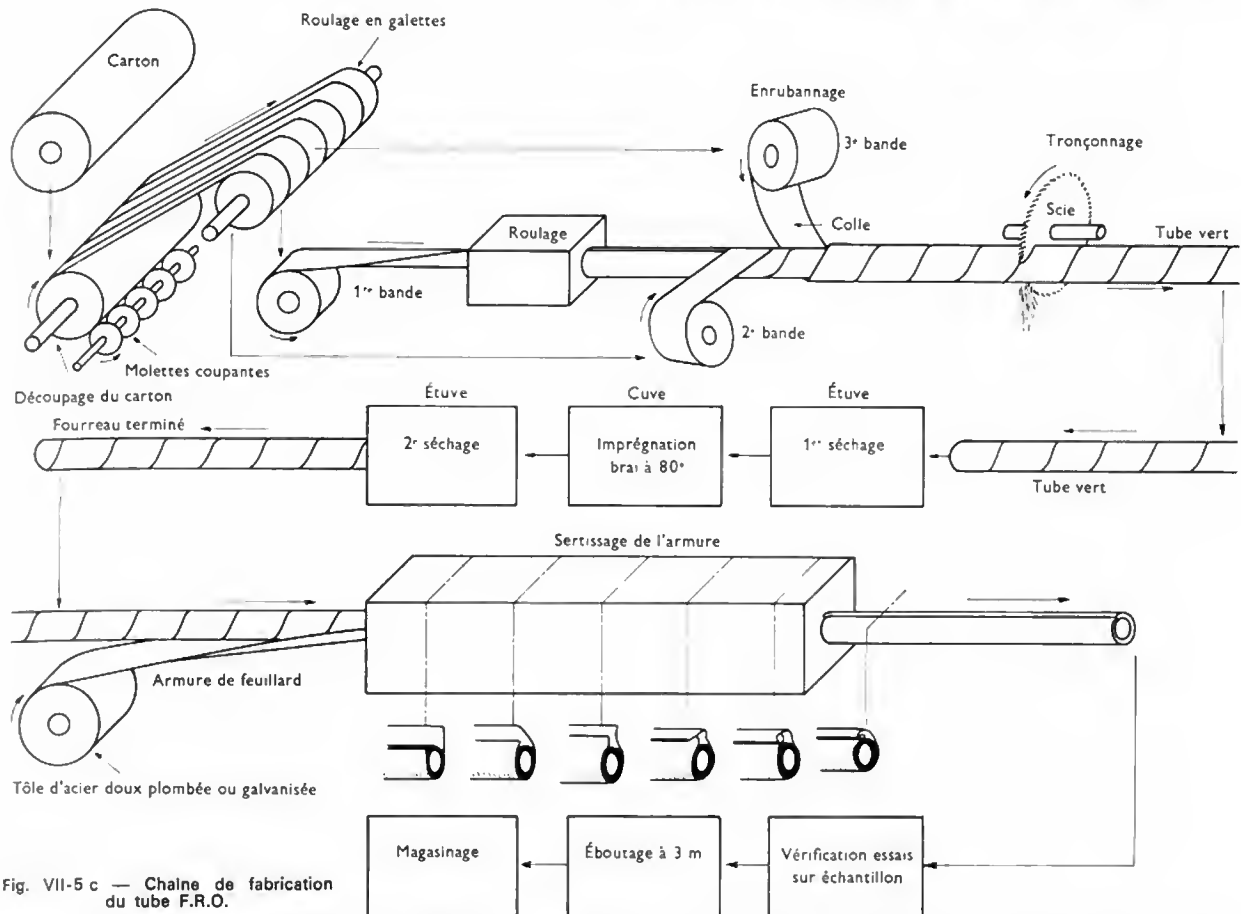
c — Chaîne de fabrication du tube F.R.O.
